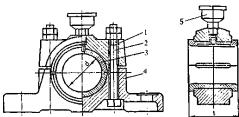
Подшипник скольжения с разъемным корпусом
